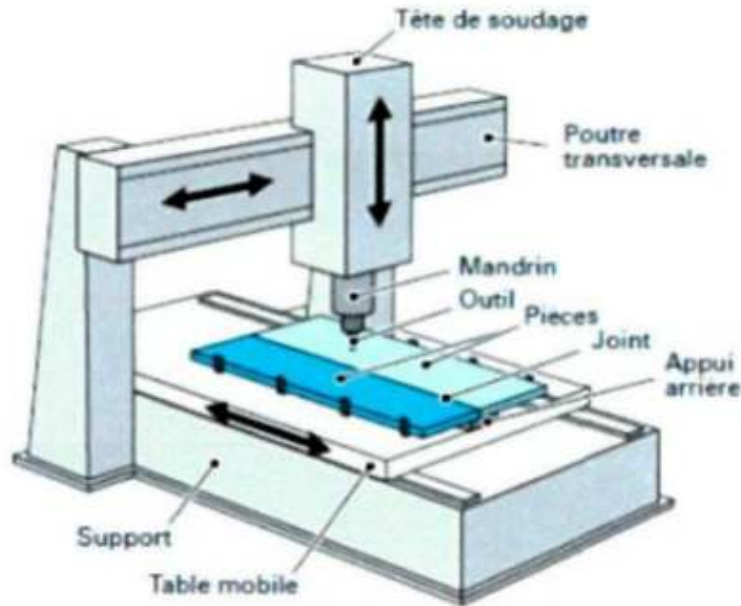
Machine typique pour le soudage par friction malaxage (4)
